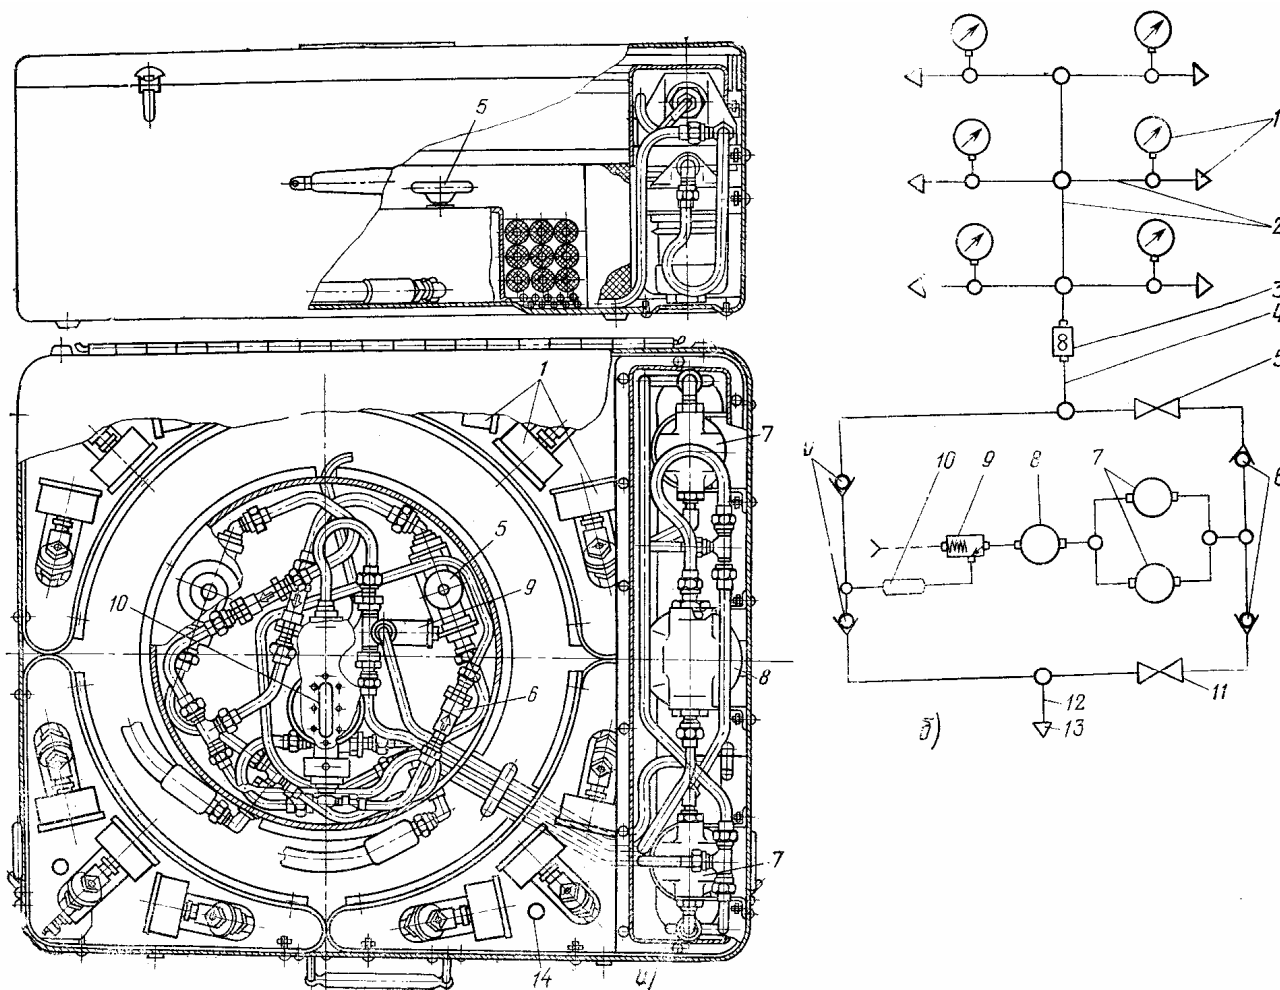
Приспособление 45.00.9956.000 для прокачки тормозной системы:
